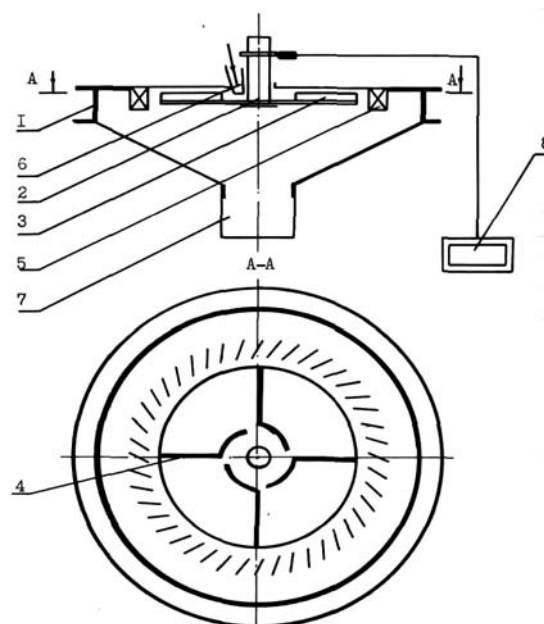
Принципиальная схема центробежного ускорителя: 1 – корпус; 2 – вал; 3 – ротор; 4 – разгонная лопатка; 5 – неподвижная плита; 6 – загрузочный патрубок; 7 – выгрузочное отверстие; 8 – электронный измеритель скорости ТСА
